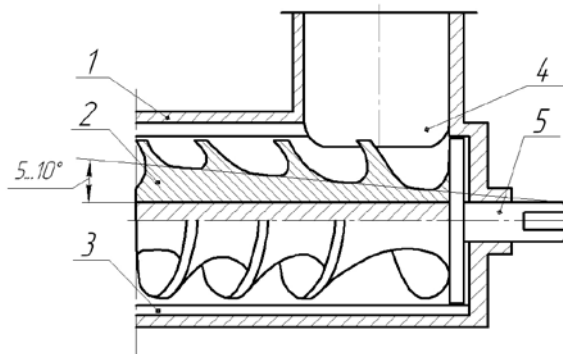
Пристрій для транспортування і подрібнення продуктів: 1 - корпус; 2 - шнек; 3 - ребра; 4 - завантажувальний бункер; 5 - вал
